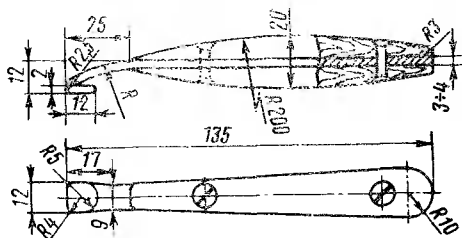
Приспособление для монтажа отделочной рамки в паз уплотнителя
